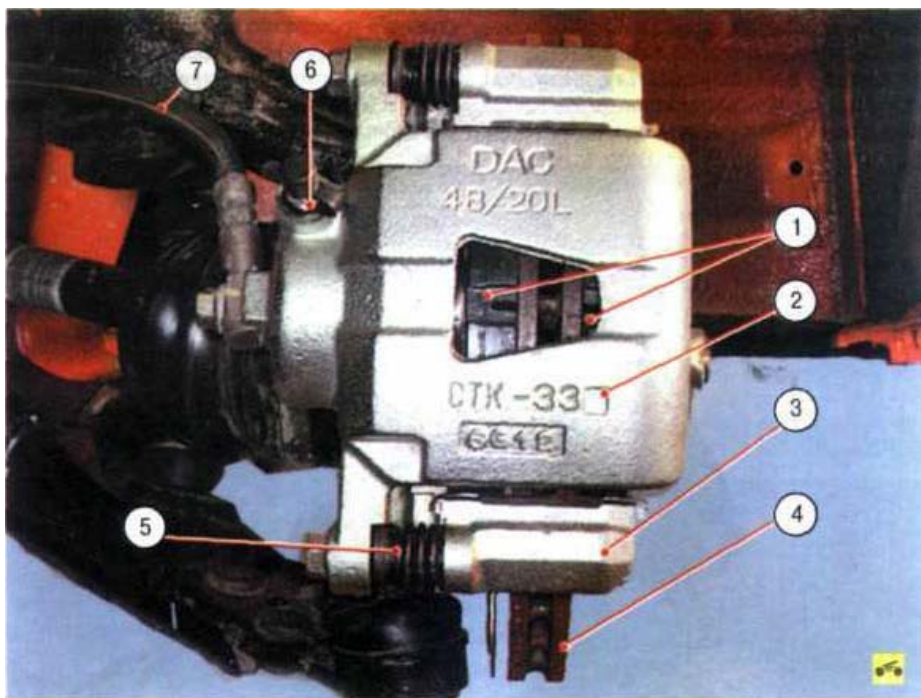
Тормозной механизм переднего колеса: 1 - тормозные колодки; 2 - суппорт тормозного механизма; 3 - направляющая колодок; 4 - тормозной диск; 5 - направляющий палец суппорта; 6 - клапан выпуска воздуха; 7 - тормозной шланг
